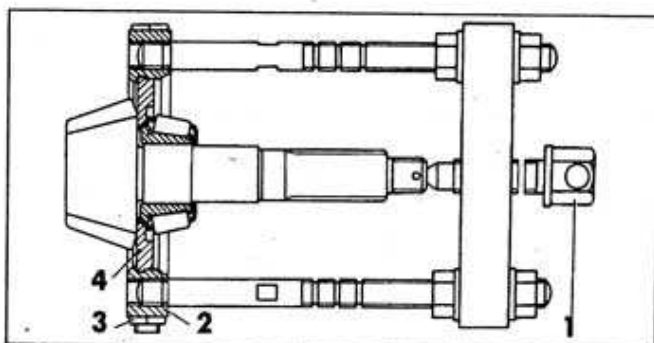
Снятие подшипника с ведущей шестерни главной передачи. 1 – винт; 2 – опора; 3 – гайка; 4 – вкладыш
